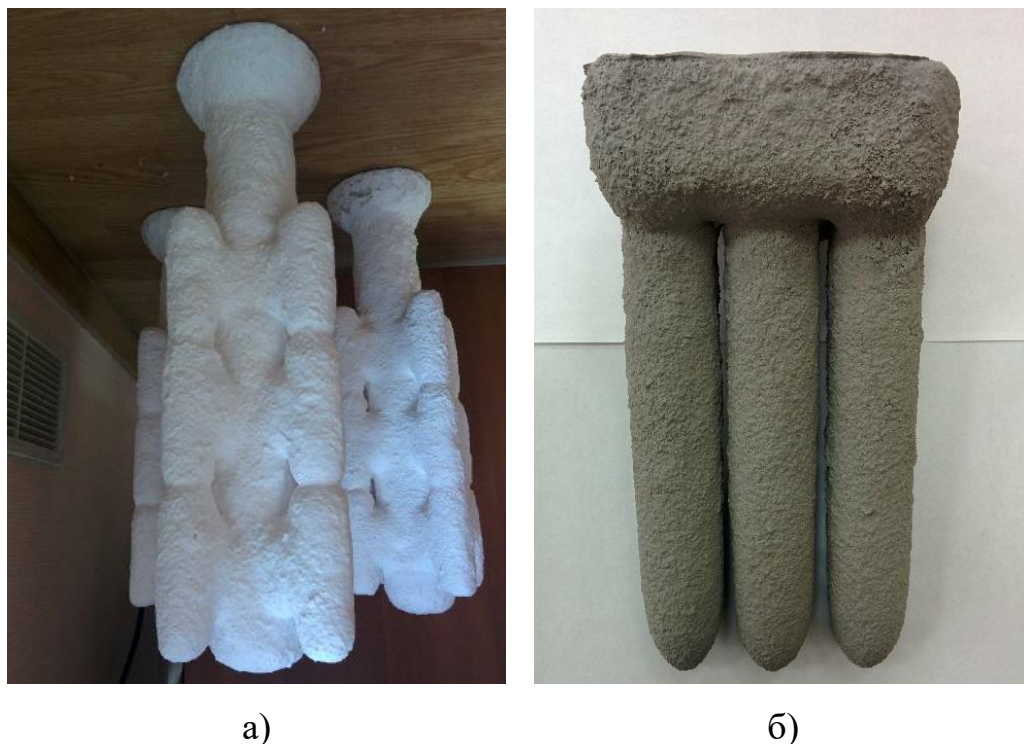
Литниковые формы для выплавки заготовок СО ЖНС методами
